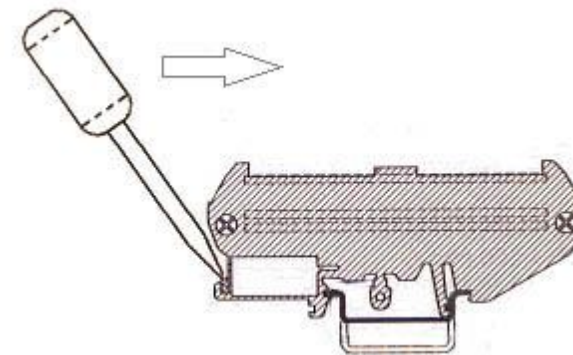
Внешний вид корпуса основного блока адаптера
